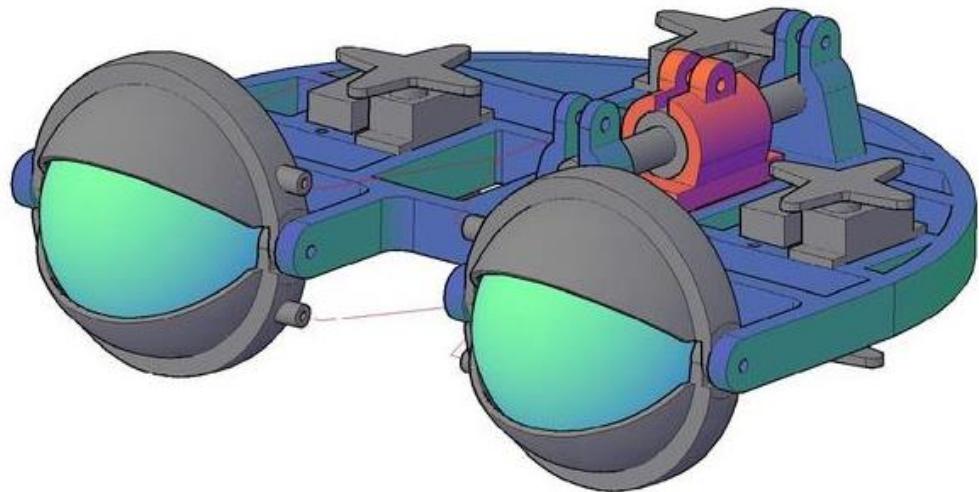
Ensamble en 3D de las piezas diseñadas
